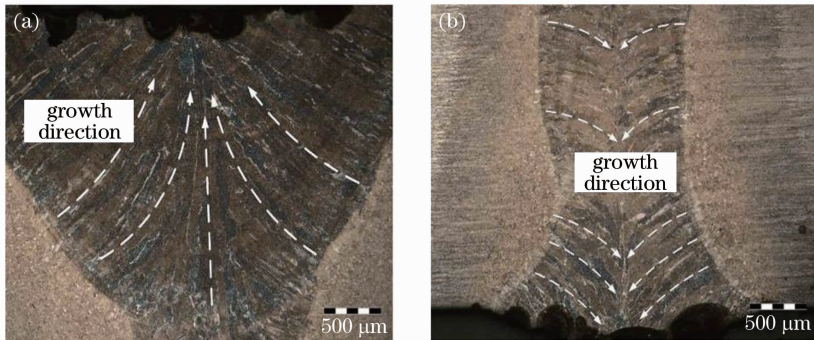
复合焊缝特征。(a)电弧区焊缝形貌;(b)激光区焊缝形貌
